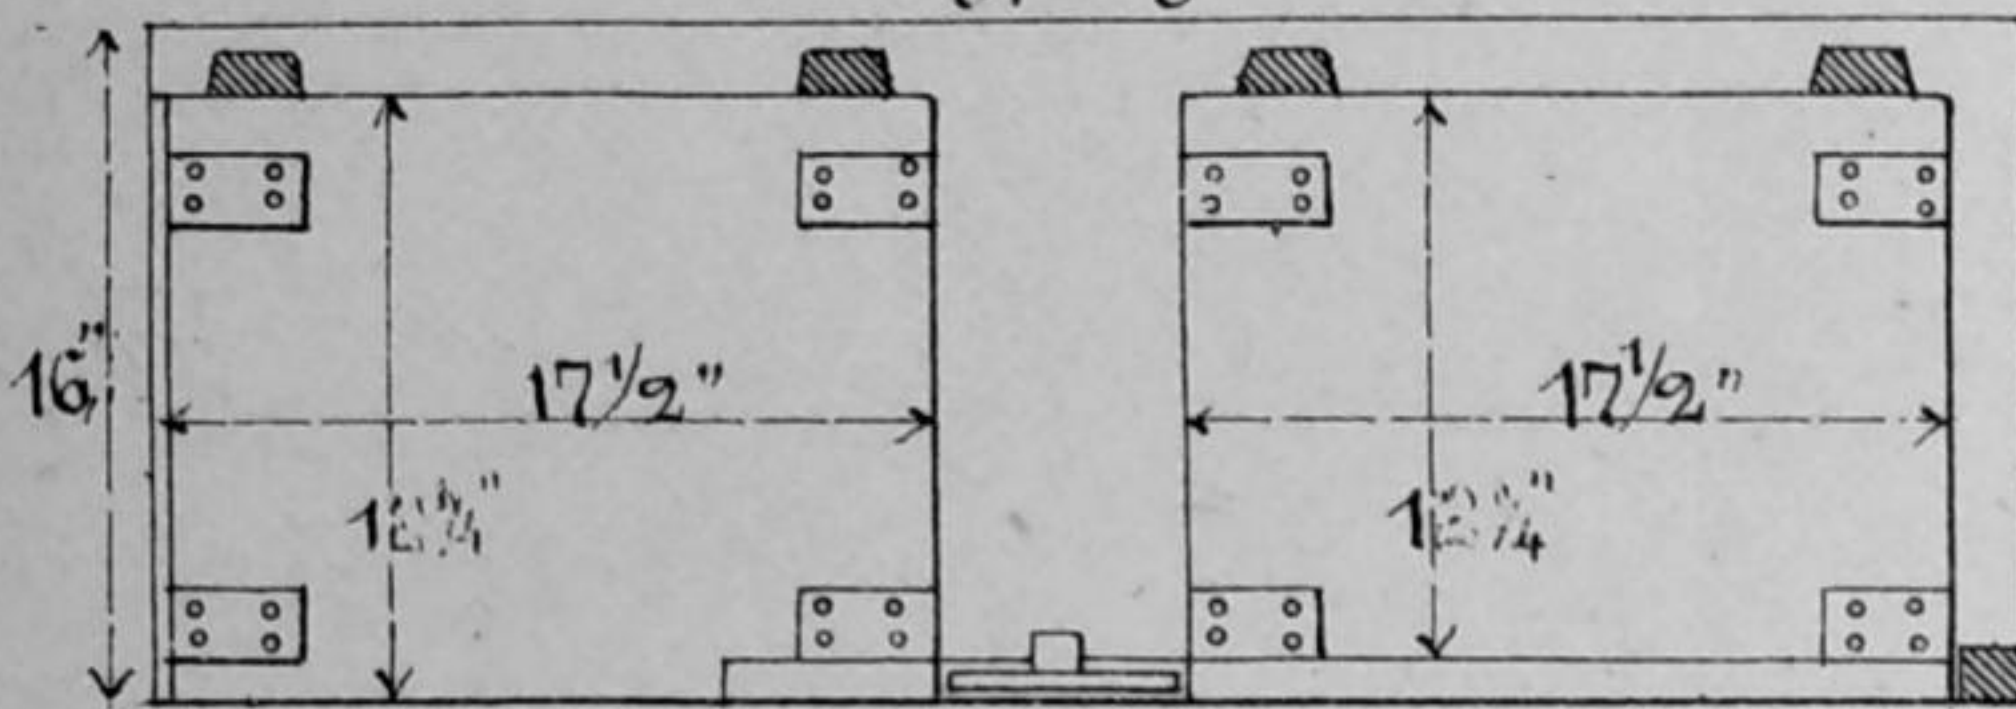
УКЛАДКА БУФЕРНОЙ ДВУКОЛКИ.
